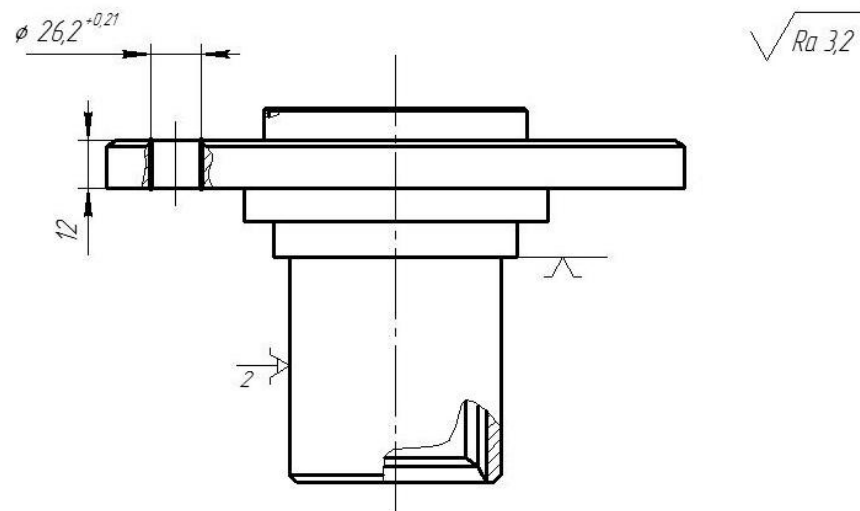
Процес свердління маточини у ході механічної обробки.
